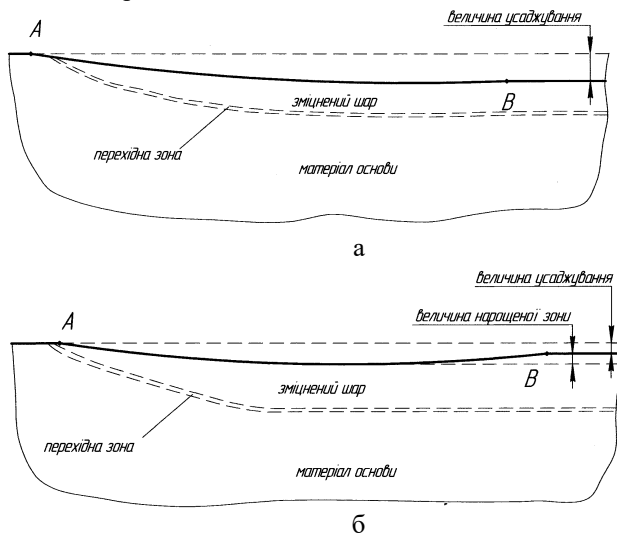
Поздовжній переріз зміцненого шару в зоні плями контакту інструмента-диска (збільшення  $\times 20$ ): а – зустрічний спосіб подачі заготовки; б – попутний; крива А-В – пляма контакту
